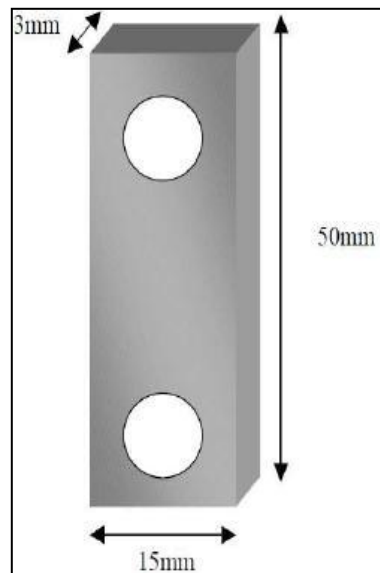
Dimensiones de probeta de corrosión empleada en los ensayos por pérdida de peso
